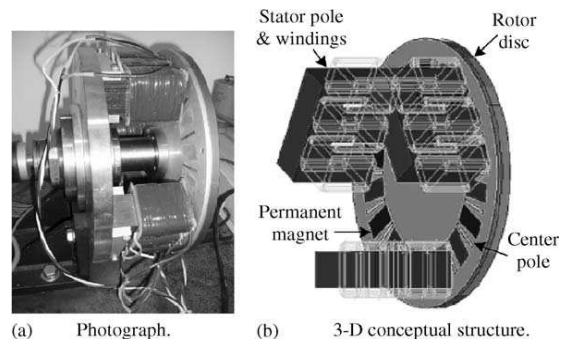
Machine discoïde 1 stator / 1 rotor à bobinage sur dents et pôles centrés [LIU 06]
